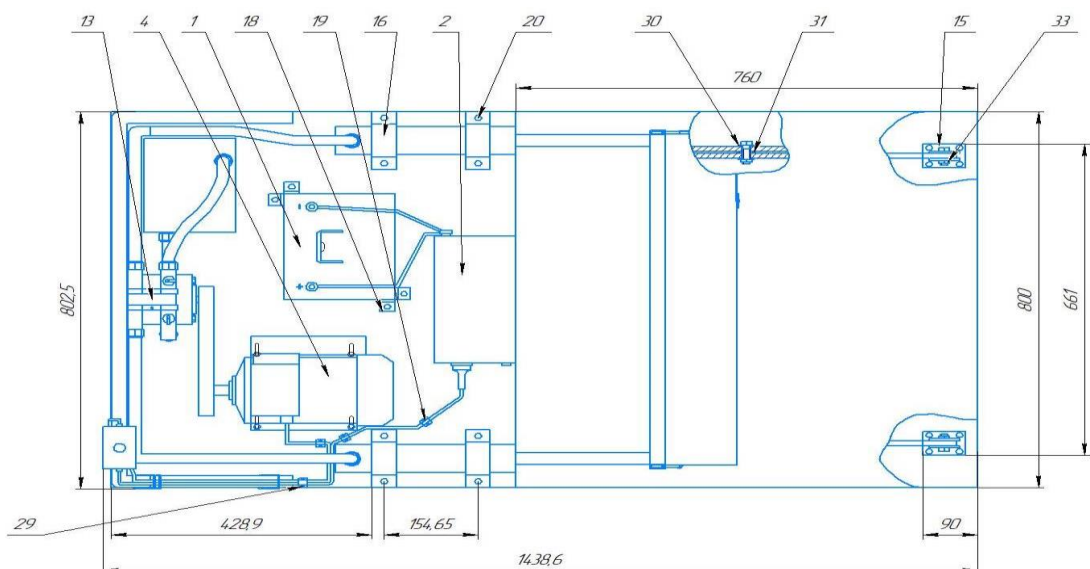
Схема разрабатываемого образца (вид сверху)
